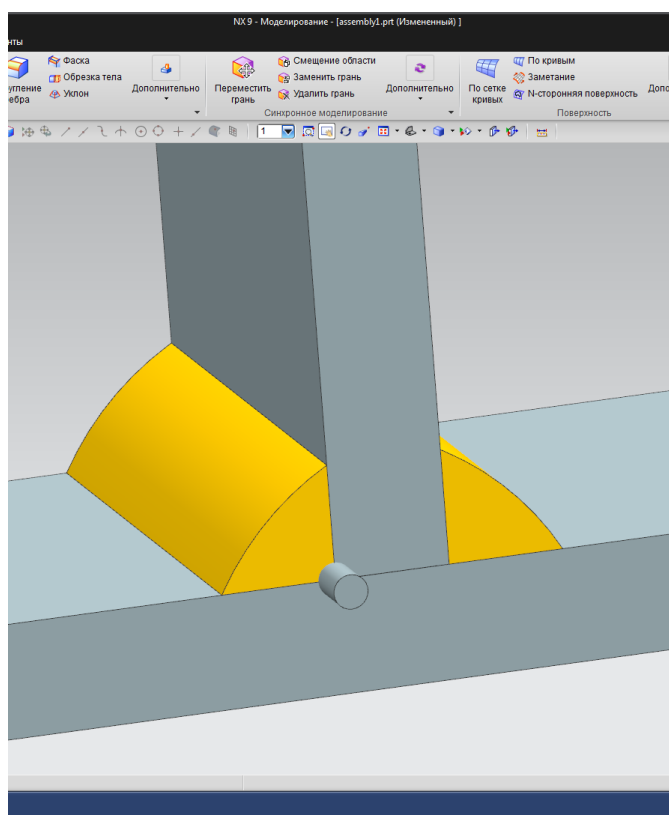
Цилиндр в корне сварного соединения
